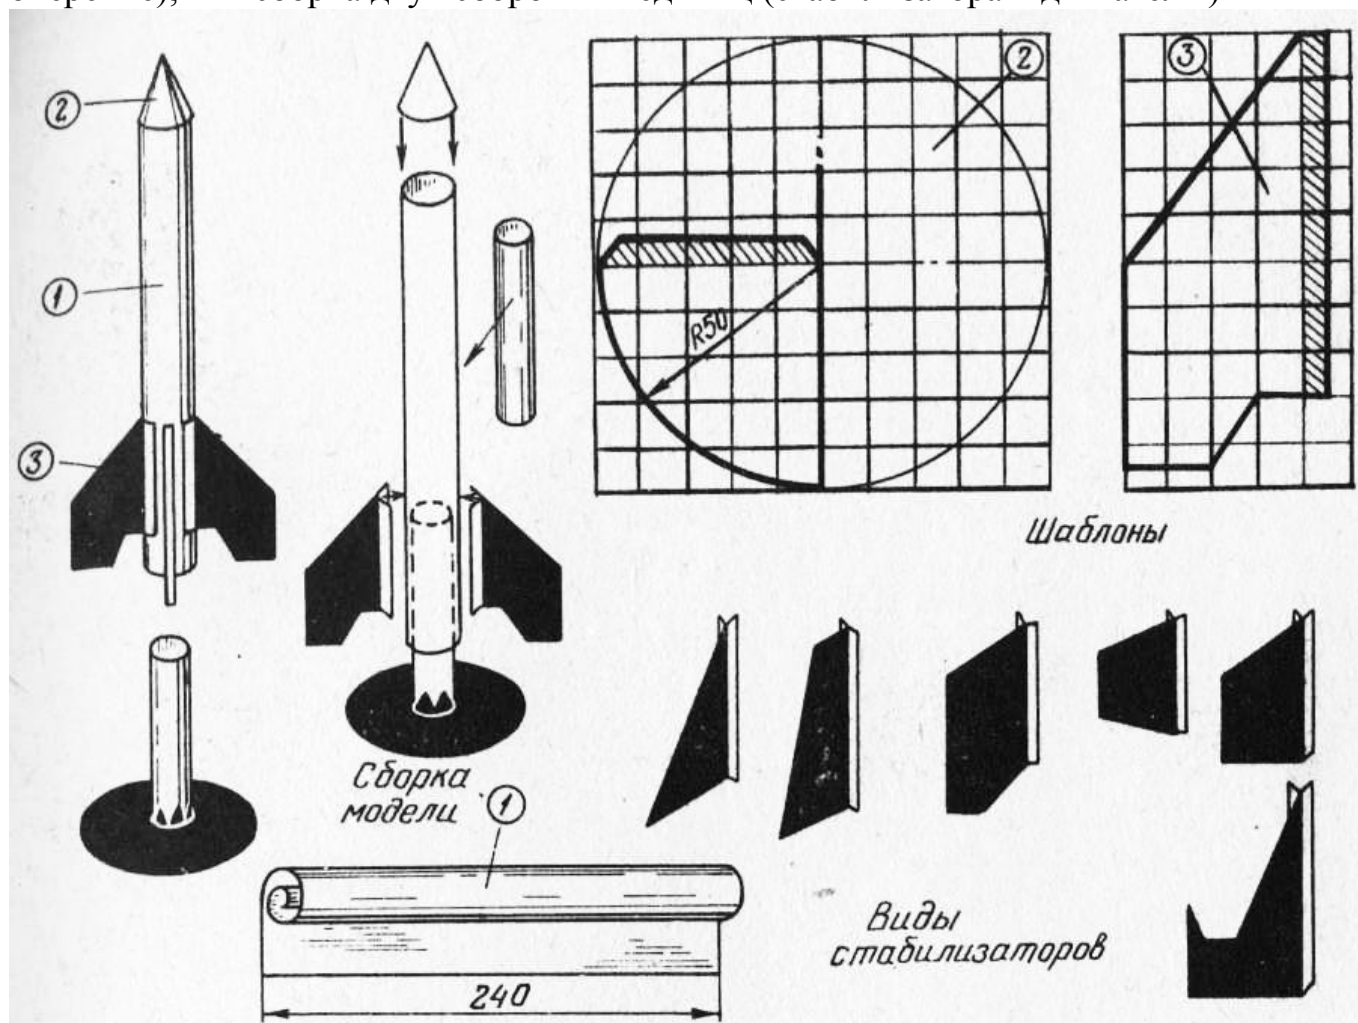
Модель ракеты с конической головкой: 1 — корпус; 2 — головная часть ракеты; 3 — стабилизатор
